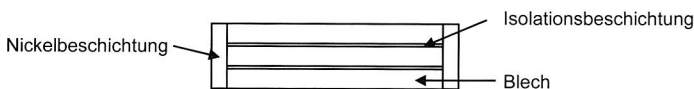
Schnittansicht eines Blechpaketringkerns mit einer Nickelbeschichtung der Kanten (Beispiel mit drei Blechen)
